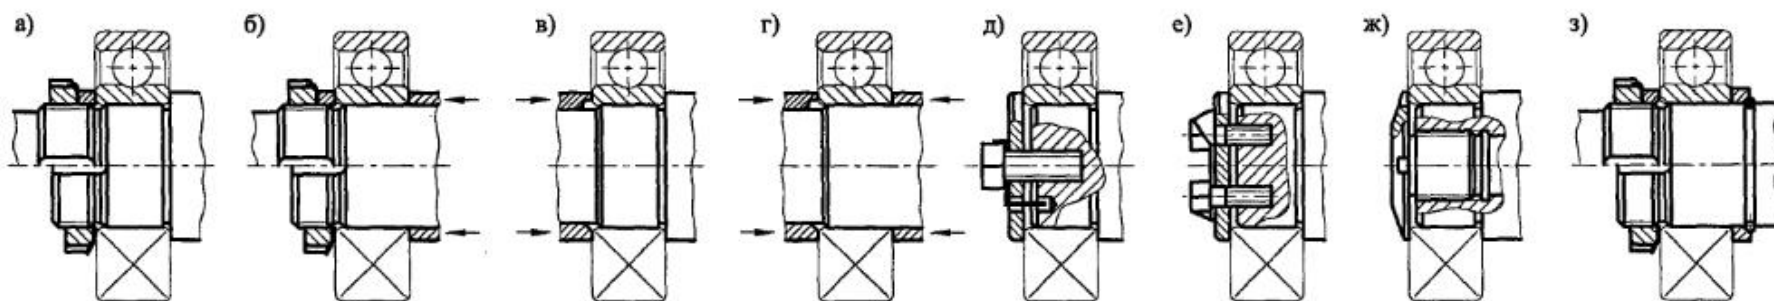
Установка подшипника на валу, обеспечивающая силовую его затяжку в осевом направлении
